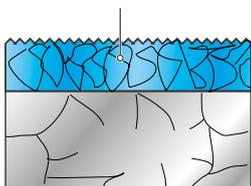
Vista in sezione del trattamento di fosfatazione sulla gabbia in lamiera d'acciaio
